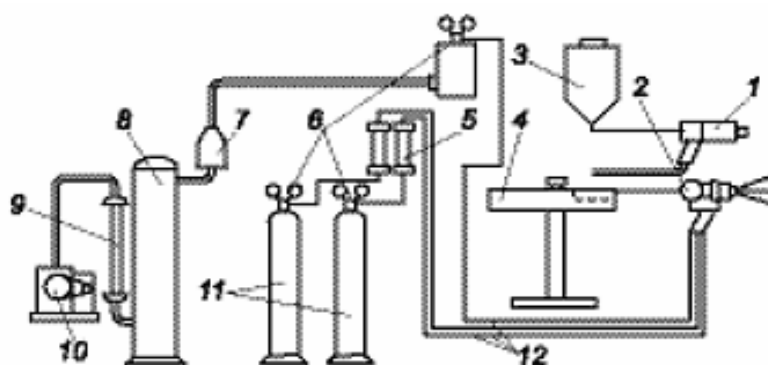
Схема установки для сверхзвукового газопламенного напыления
